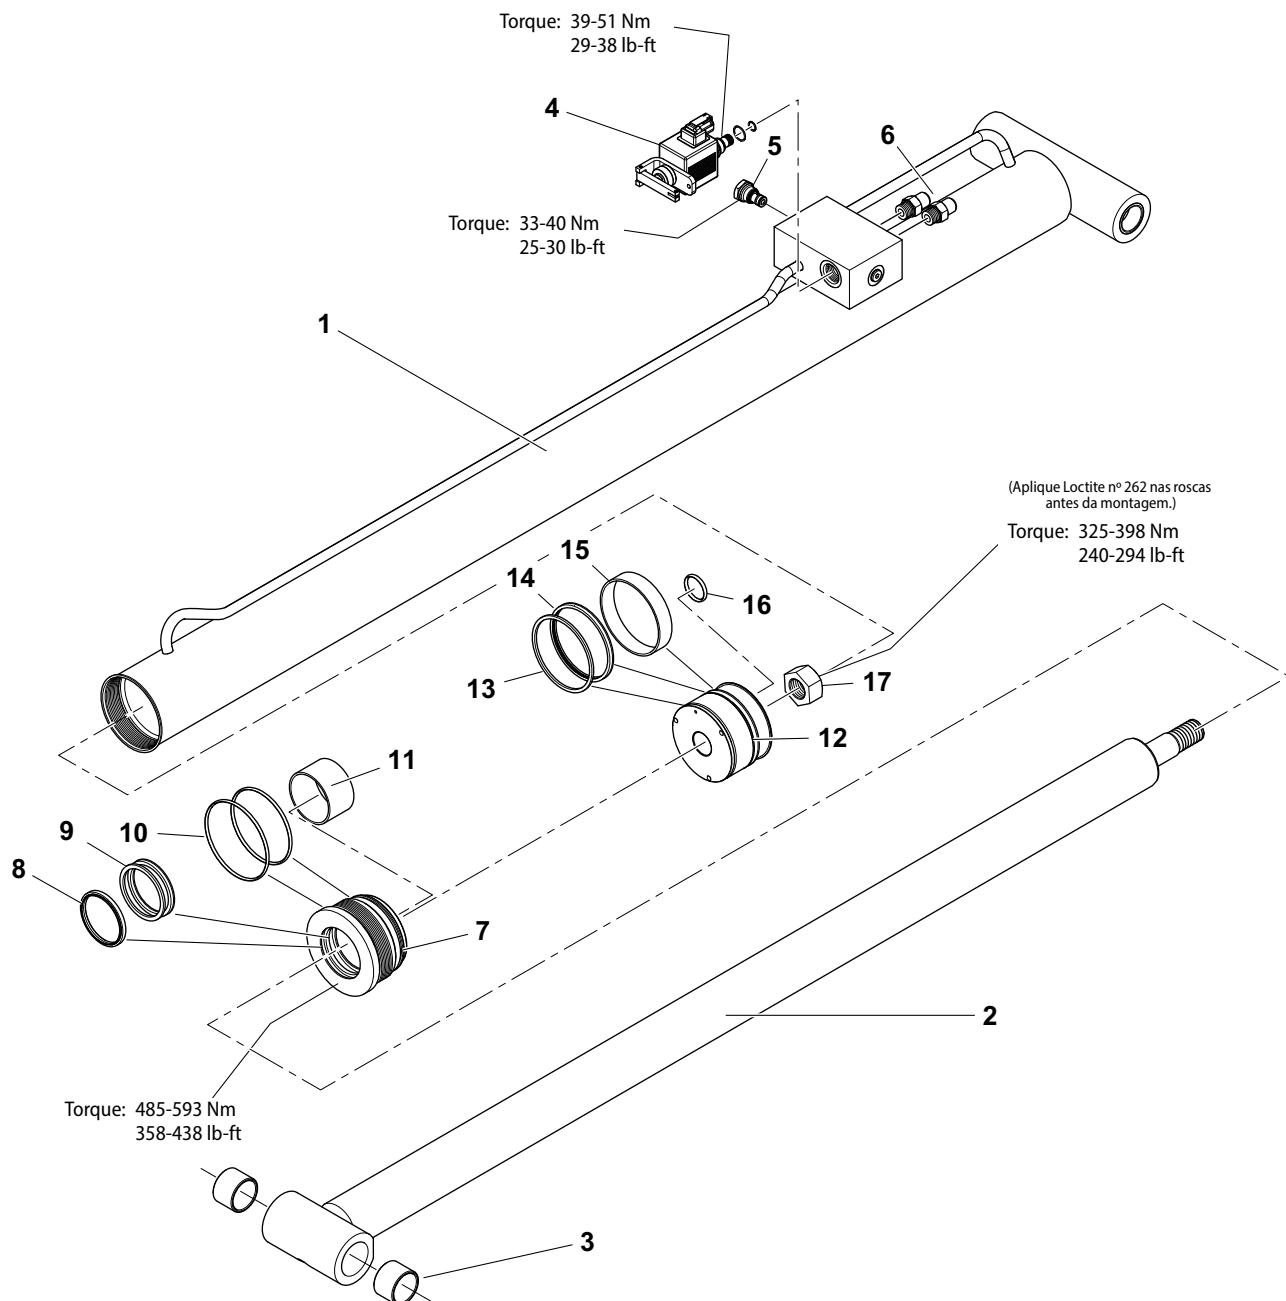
1932RS/6RS - Cilindro de elevação
